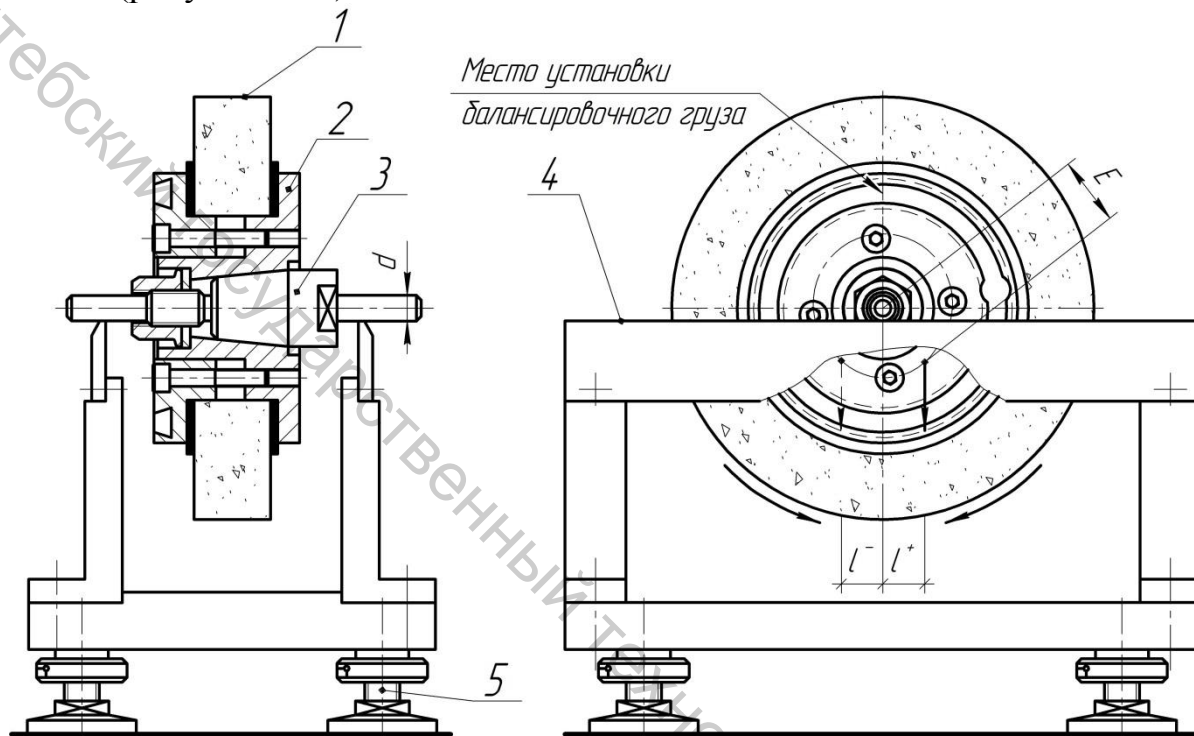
Статическая балансировка шлифовального круга с переходными фланцами в сборе: 1 – круг шлифовальный; 2 – фланцы переходные; 3 – балансировочная оправка; 4 – опорные ножи балансировочного приспособления; 5 – регулируемые винтовые опоры; E – радиальное смещение центра масс системы круг – планшайба;  $l^-$ ,  $l^+$  – плечи моментов дисбаланса масс в неустойчивом положении системы круг – планшайба
